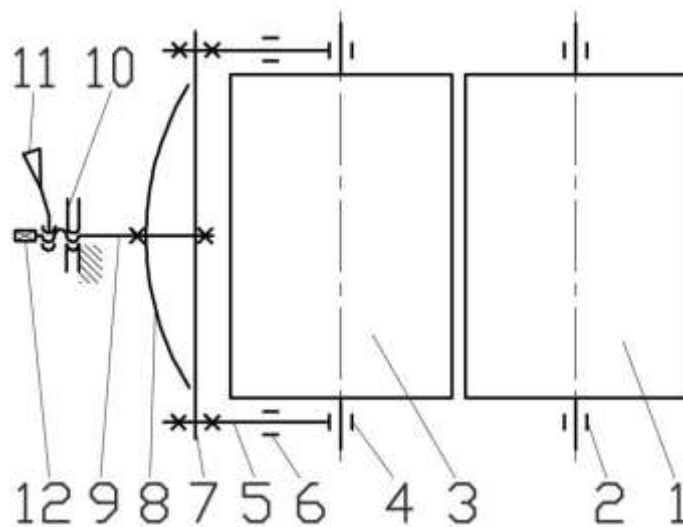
Схема вальцьової дробарки.
